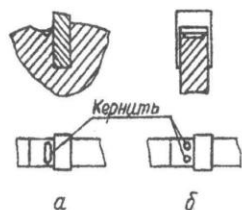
Дополнительное крепление режущих пластин кернением: а - продольным; б - точечным
